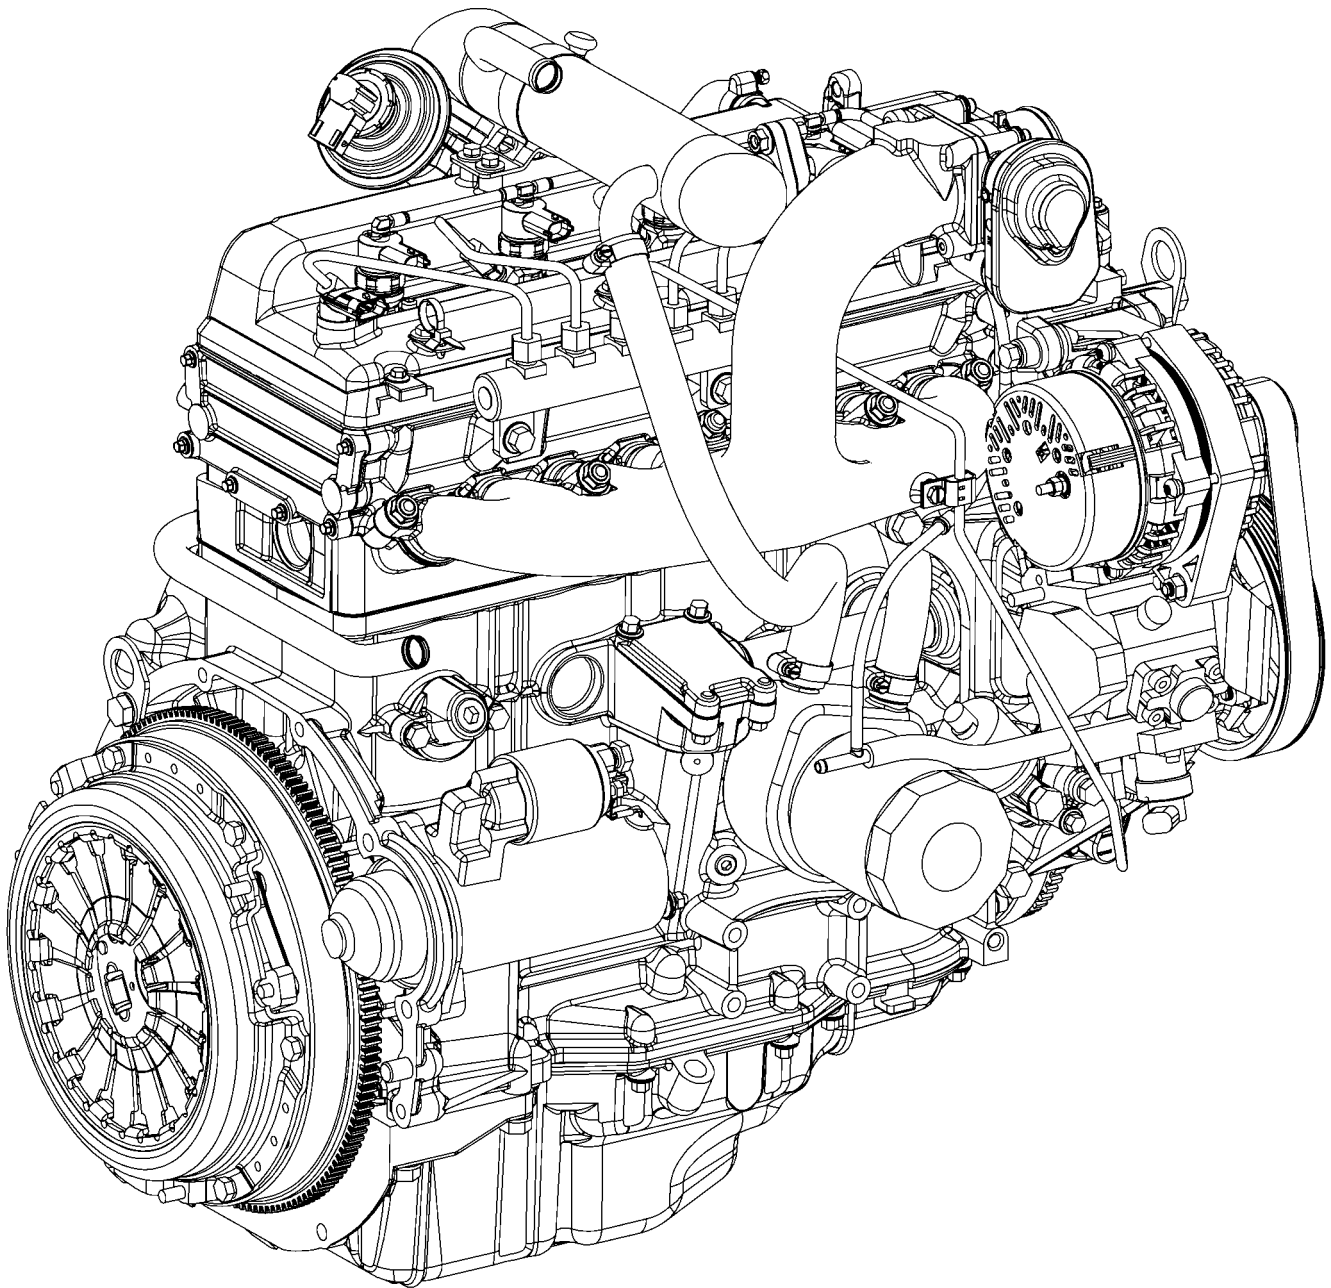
в. Внешний вид двигателя без компрессора кондиционера, насоса ГУР и деталей привода вентилятора
